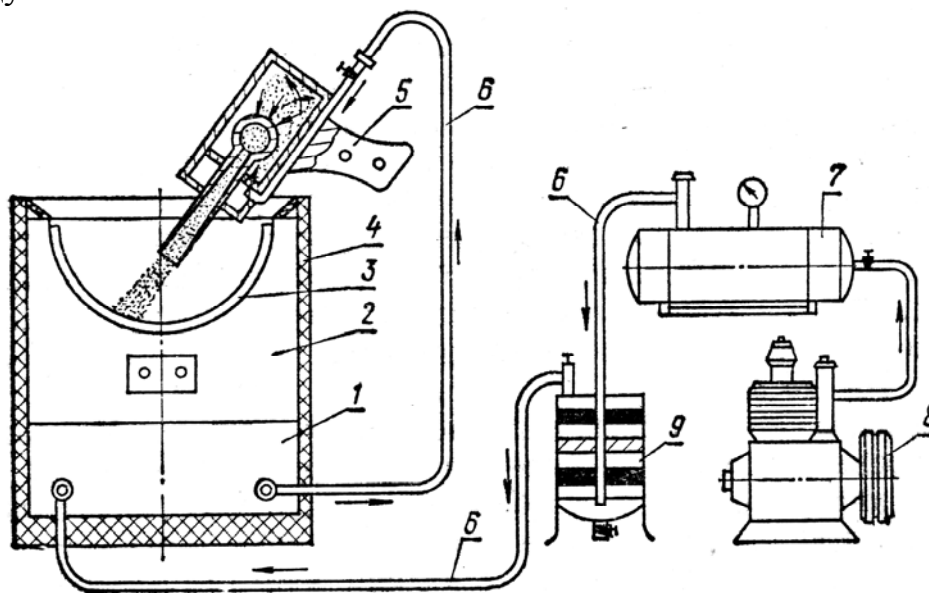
Схема установки для нанесения порошков пластмассы на вкладыши подшипников коленчатого вала:
